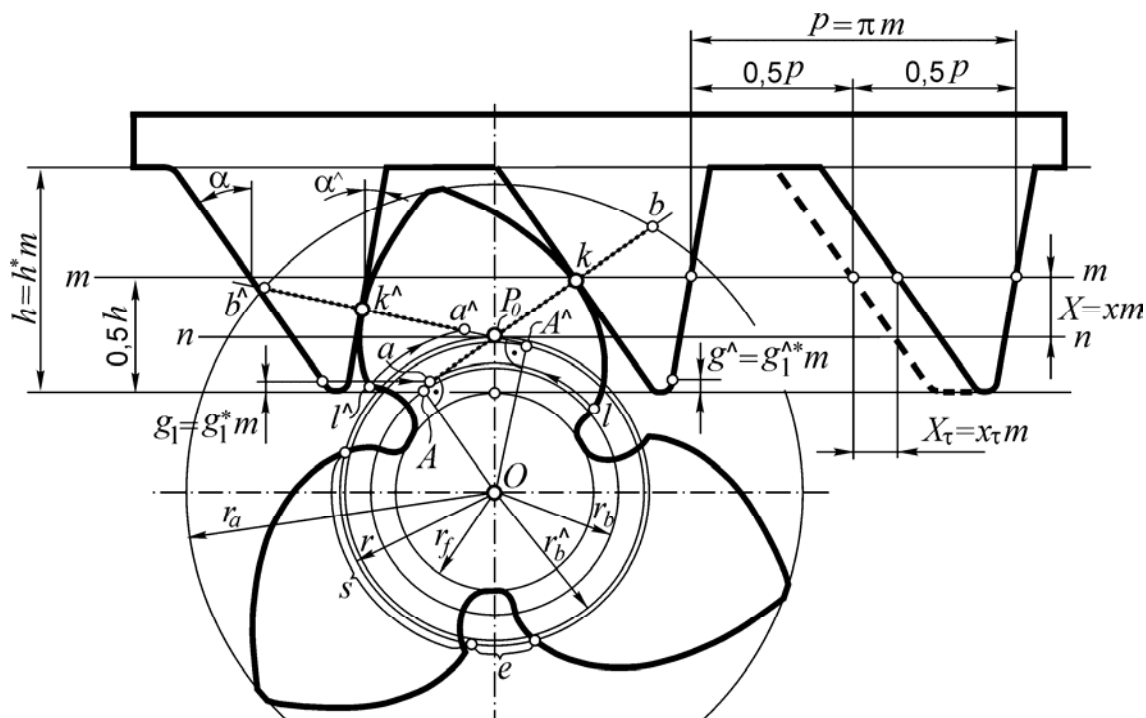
Станочное зацепление шестерни с производящей рейкой
